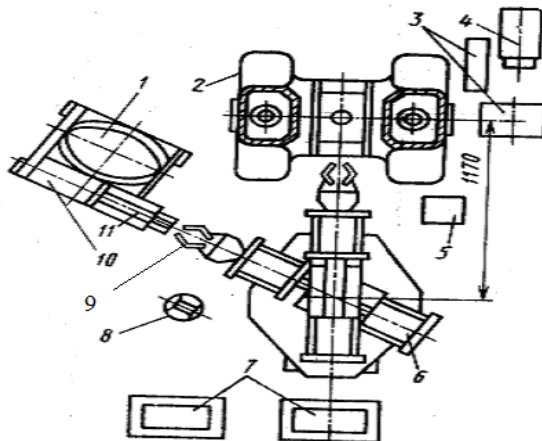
Схема РТК для горячей штамповки из штучной заготовки:
